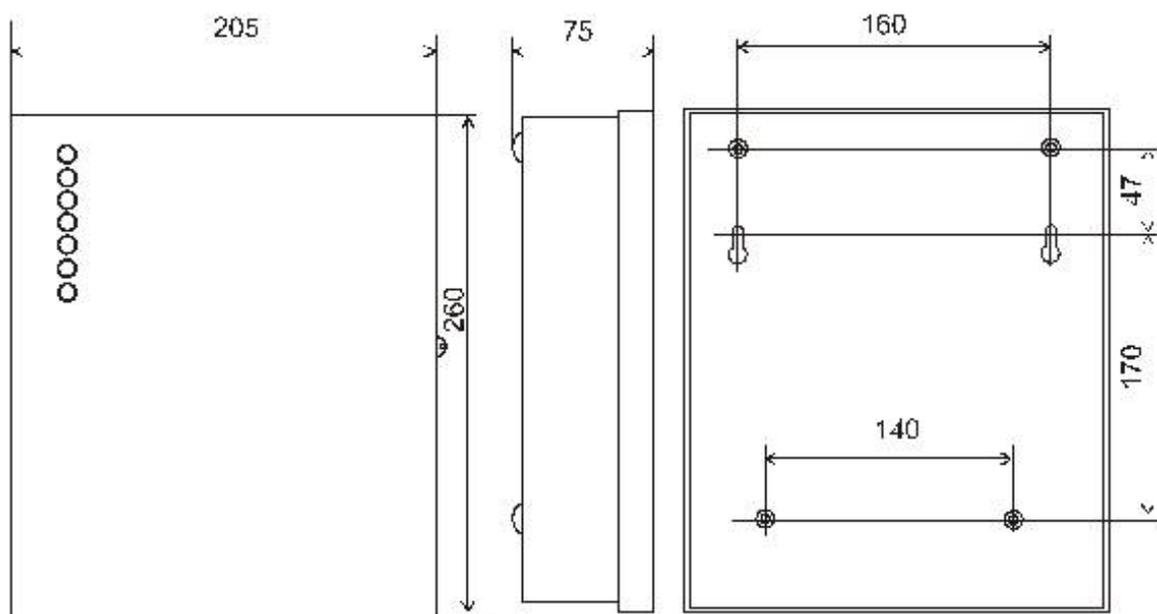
Габаритные и установочные размеры прибора, металлический корпус
